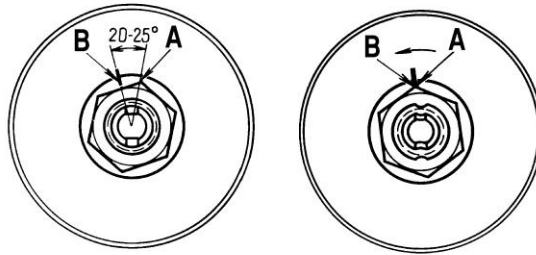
Затягування й регулювання підшипників маточини переднього колеса
